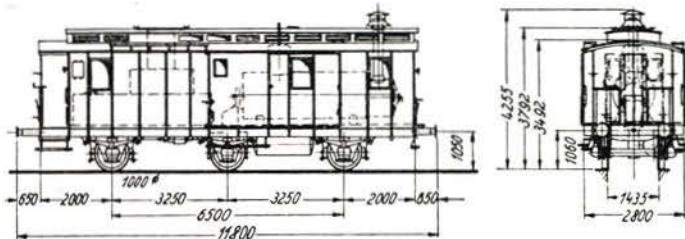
Dreiachsiger Heizkesselwagen, Baujahr 1914/15, zur Zeit noch in Betrieb
